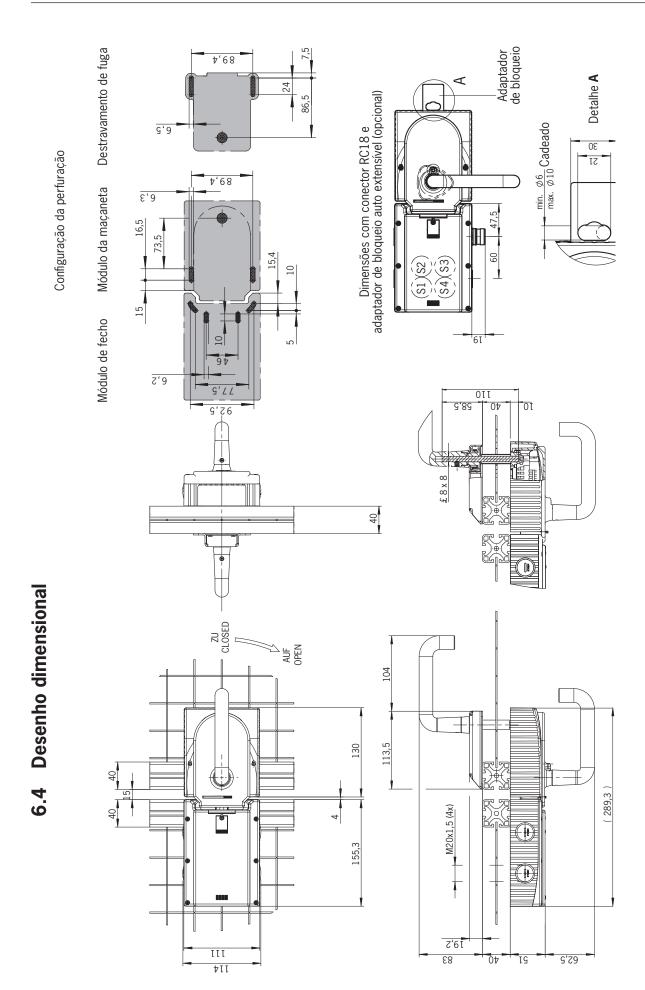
Desenho dimensional MGB montado, sem placas de montagem opcionais
